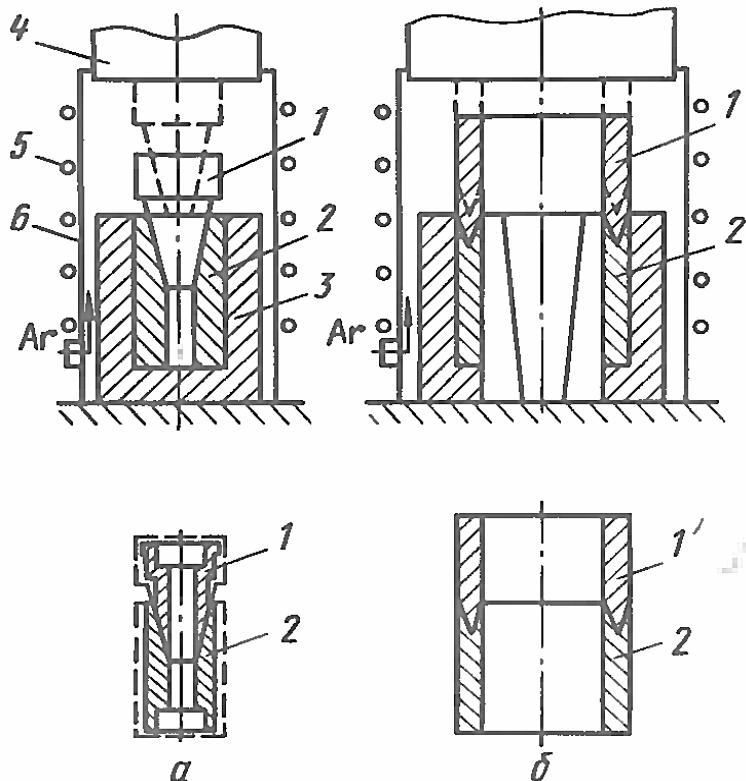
Различные виды технологических схем клинопрессовой сварки трубчатых переходников малого (а) и большого (б) диаметра из разнородных материалов: 1 – деталь из более твердого материала; 2 – деталь из более мягкого материала; 3 – прессформа; 4 – шток пресса; 5 – нагреватель; 6 – корпус камеры
